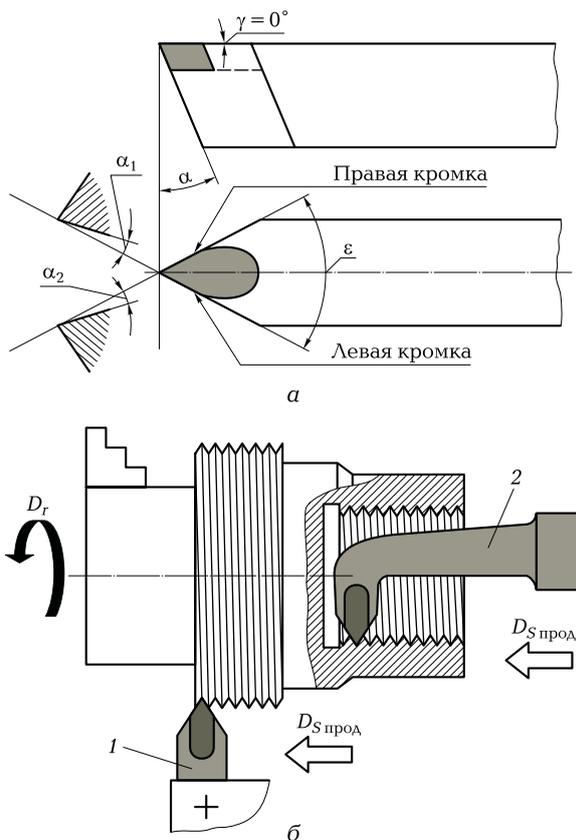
Конструкция резьбового резца и нарезание резьбовых поверхностей:
